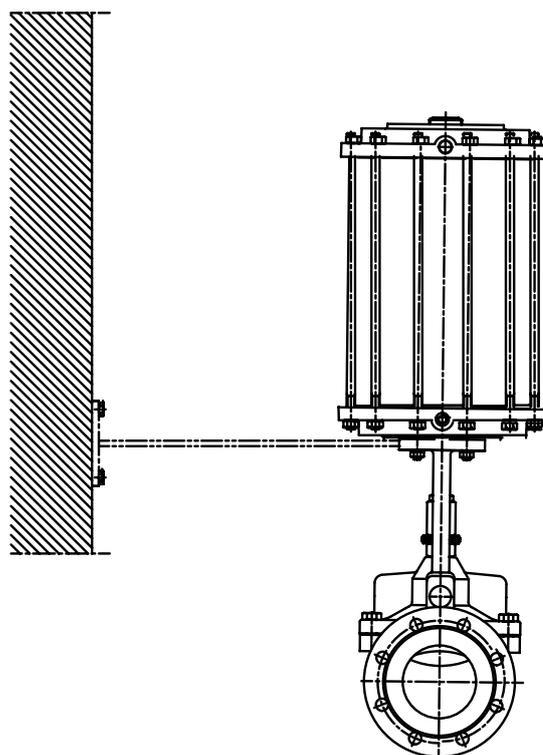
схема крепления опор к пневматическому приводу - вертикально
